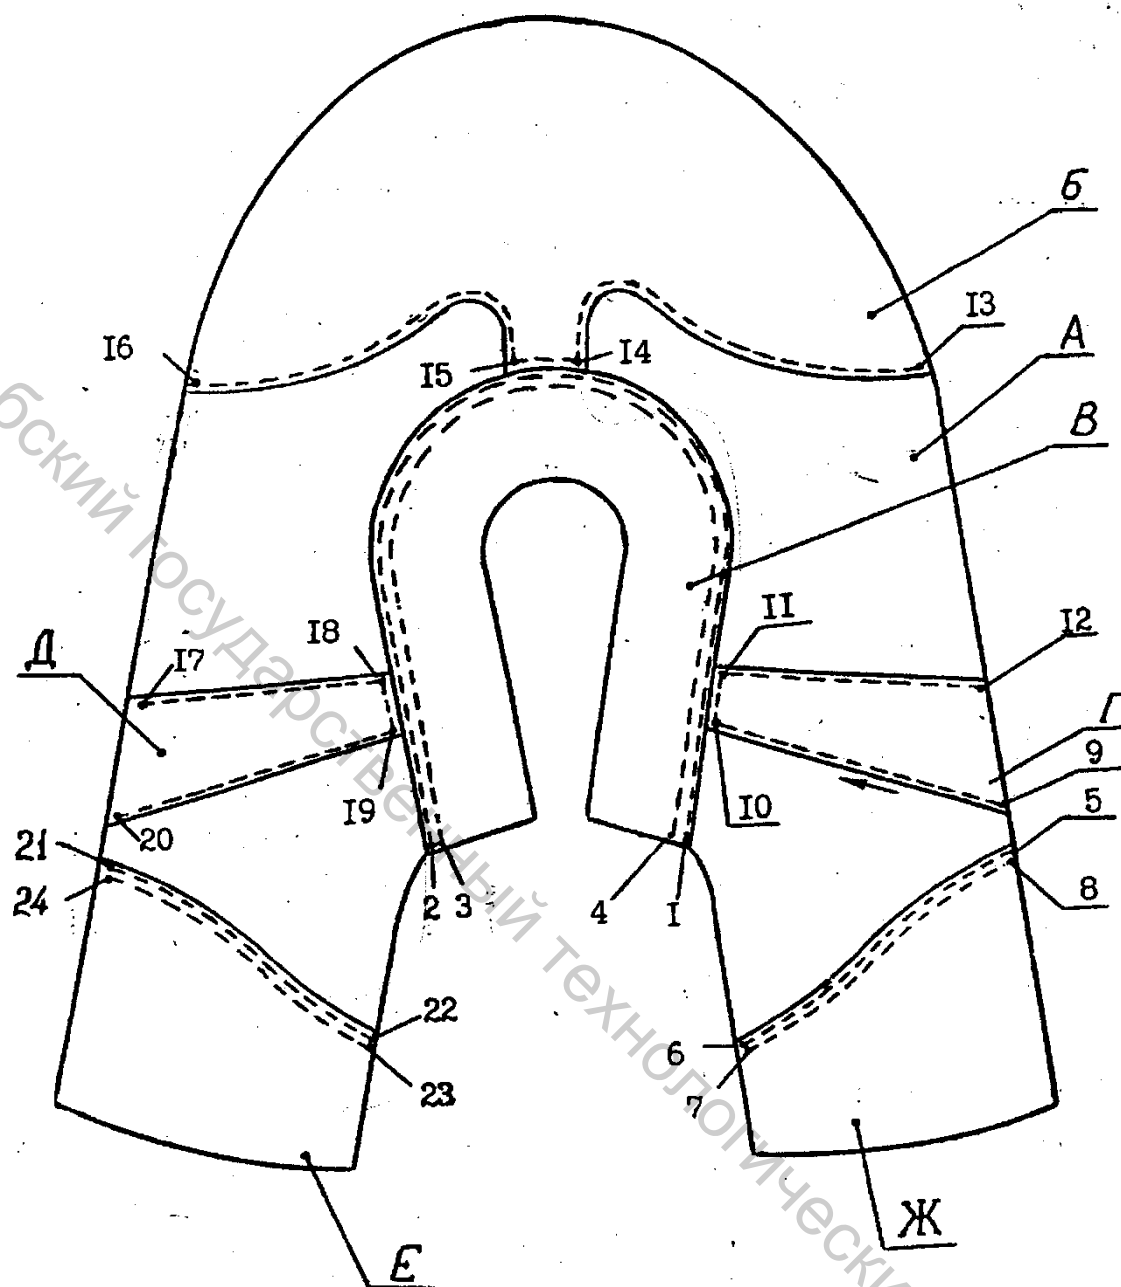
Заготовка верха обуви с контурами соединительных швов
